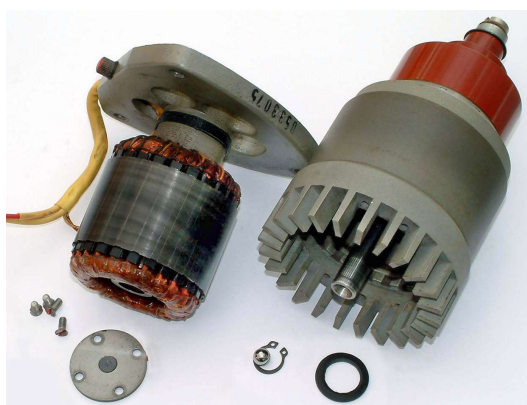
(RECHTS): M 5-Tonmotor, Außenläufer der Firma Papst. Motor demontiert. Lager: radial Gleitlager, axial die übliche einzige Kugel unter der Welle. Die Schmierung geschah von der Laufwerkoberseite nach Lösen der Schraube über den Stufenscheiben. Das Öl trat durch eine Querbohrung in die radiale Lauffläche der Mittelachse und sammelte sich in einem „Ölsumpf“ am Fuß der Welle - in Höhe der einzelnen Kugel.
